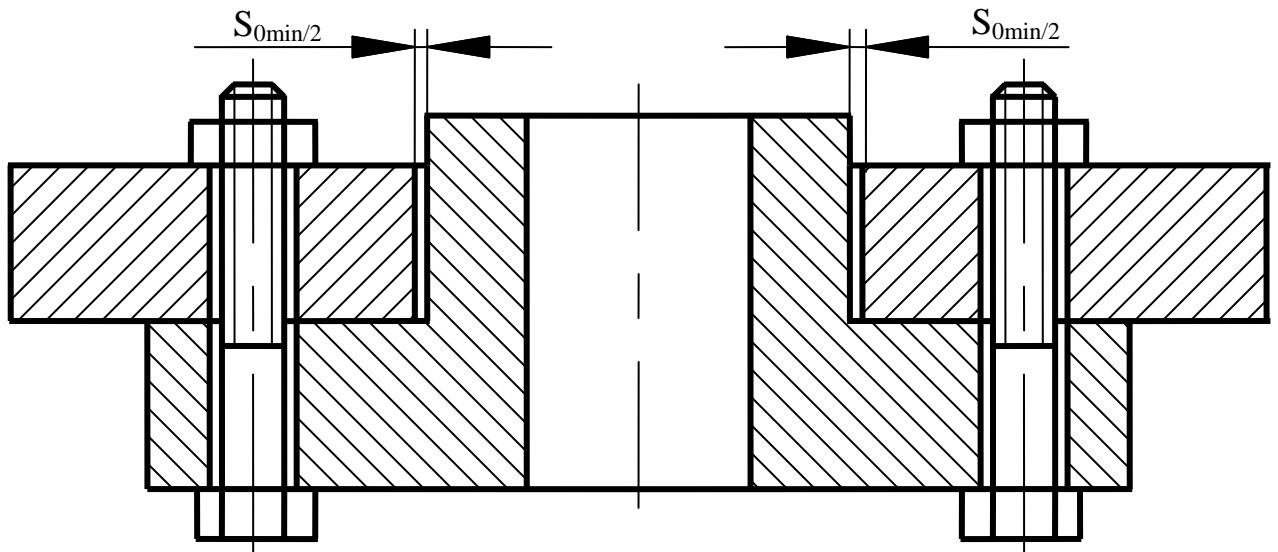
З'єднання кріпильними деталями з центруючими (базовими) елементами
